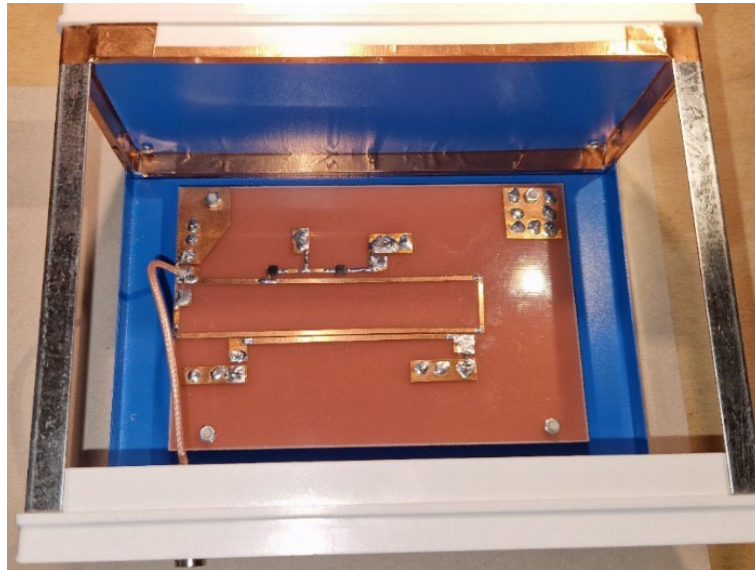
In das Gehäuse eingebaute Baugruppe, Signaleinspeisung über Koaxialkabel in die Leiterschleife.
